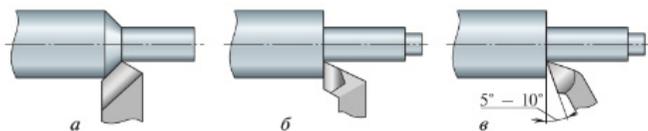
Подрезание и обтачивание уступов: *а* — проходным резцом; *б* — подрезным резцом; *в* — упорным резцом
